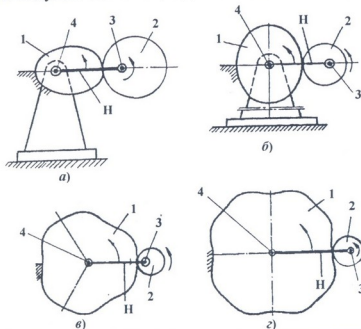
Планетарные передачи с эксцентричными цилиндрическими зубчатыми колесами
